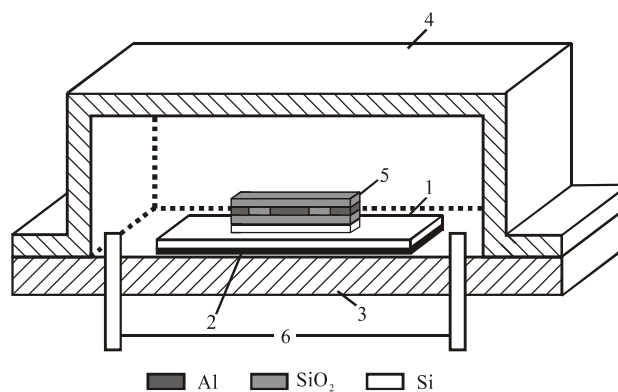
Модель микросхемы и кристалла: 1 – подложка; 2 – слой клея; 3 – основание корпуса; 4 – крышка корпуса; 5 – кристалл; 6 – выводы
